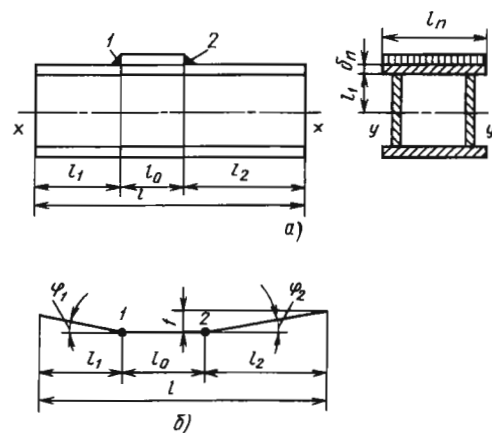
Схема изгиба сварной балки вследствие усадки поперечных швов
